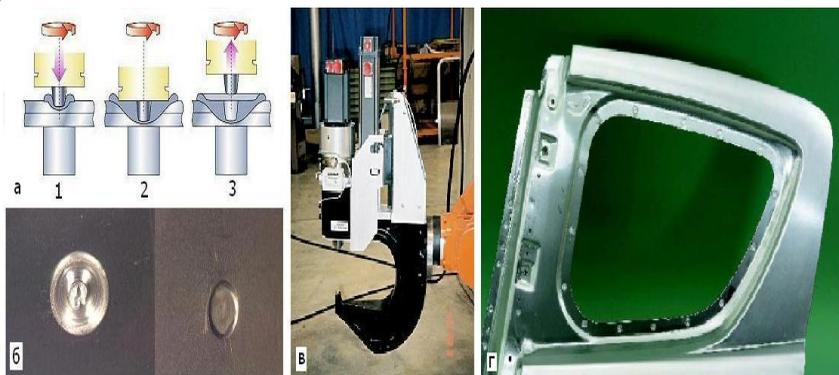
Схема процесса точечной сварки трением (а), лицевая и обратная стороны сварного соединения (б), сварочное устройство (в) и пример сварного соединения двери автомобиля Mazda (г).
